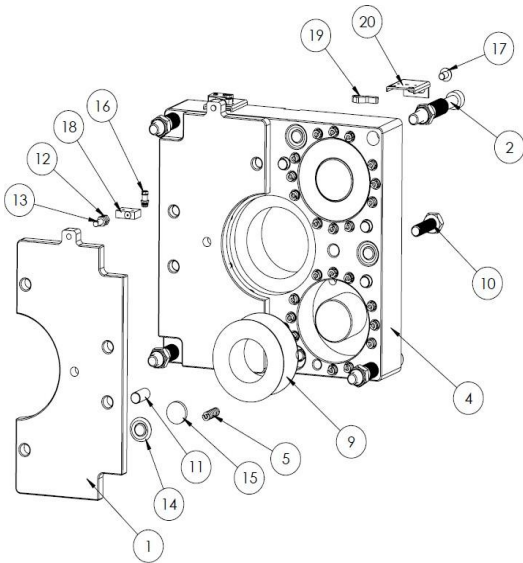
Vista en despiece del conjunto de bobinas de frenos AEMF6-12
